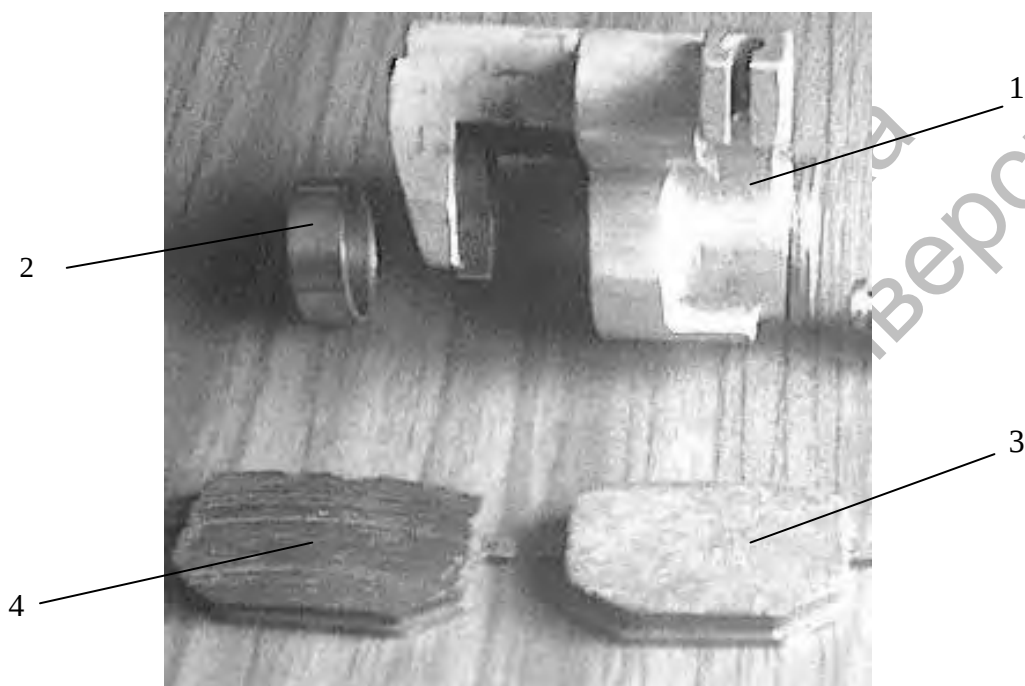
Скоба дискового тормоза с механическим приводом: 1 – скоба; 2 – цилиндр; 3 – колодка тормозная правая; 4 – тормозная колодка левая
